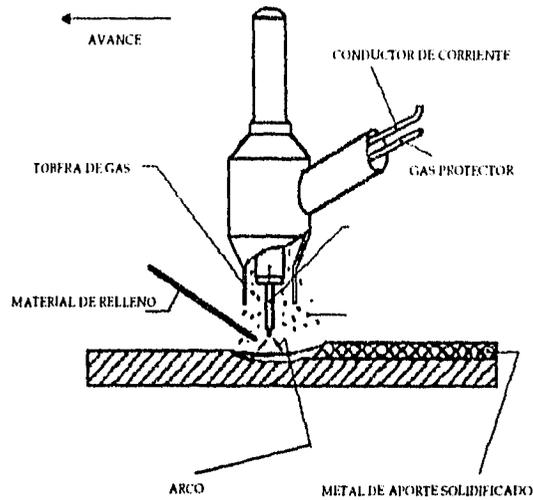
Operación de un proceso de soldadura de arco con gas y un electrodo de tungsteno.
